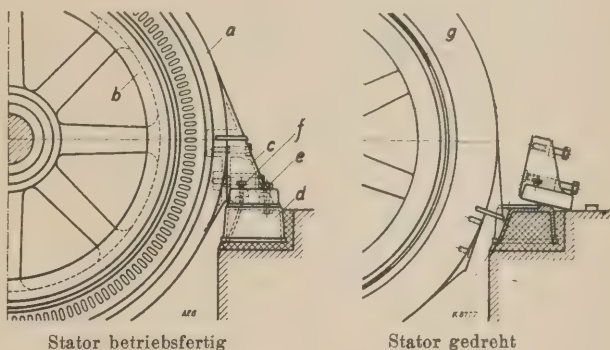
Statorgehäuse mit abschraubbaren Füßen.
